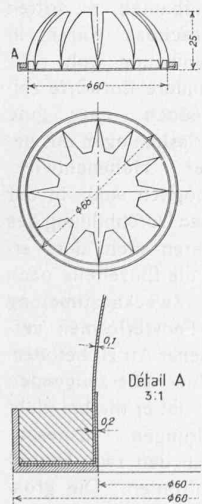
Clapet, 1 : 3. Coupe, plan et détail.
